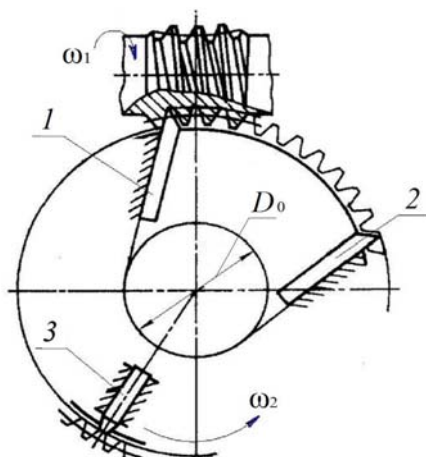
Схема трехрезцовой головки для нарезания витков глобоидного червяка:
